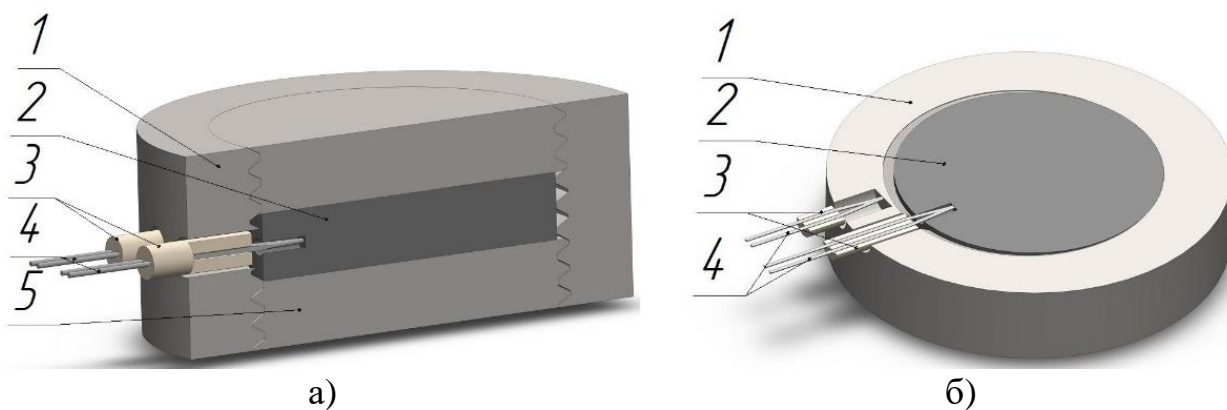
Схематический вид образца в сборке: а) поперечный разрез, б) продольный разрез: 1,5 – металлическая матрица, 2 – образец Ni–Al, 3 – керамические трубки, 4 – термопары
